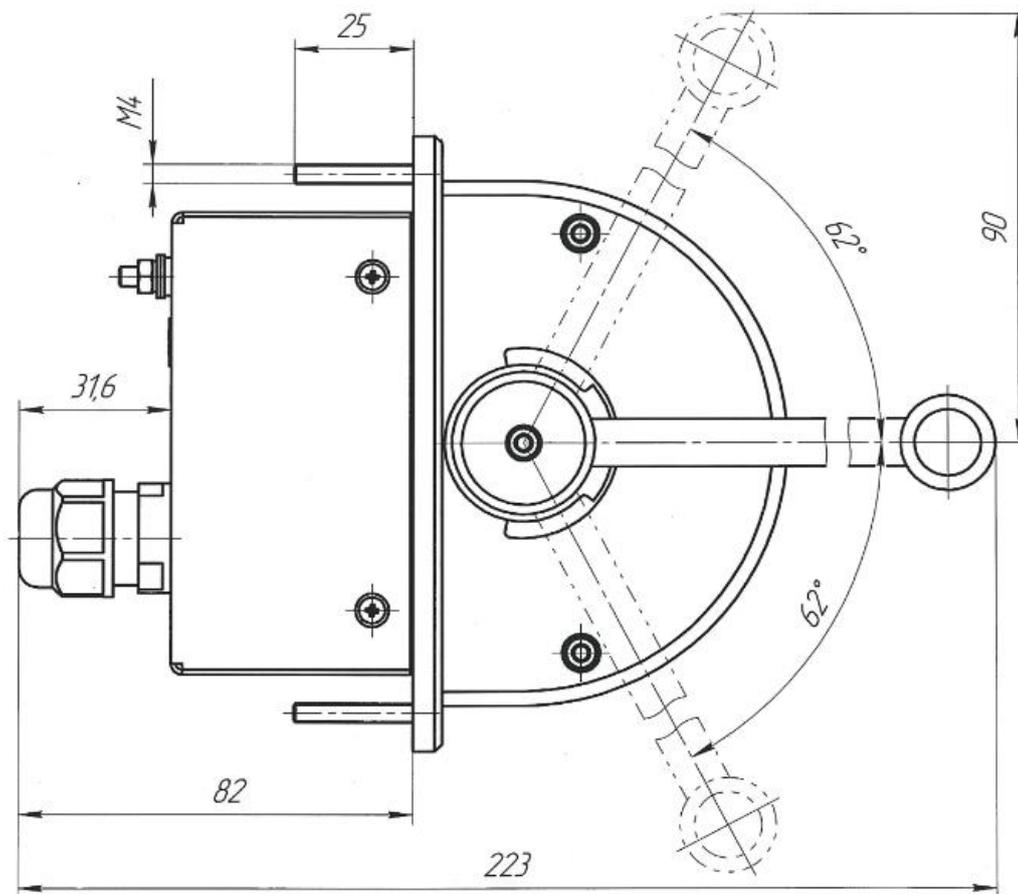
Габаритные размеры изделий типа РУС-225
